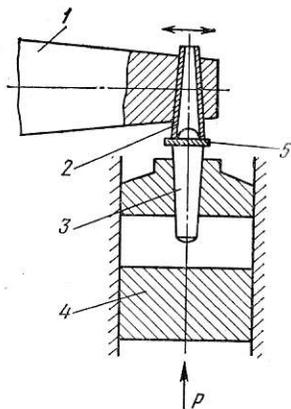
Ультразвуковая сварка по контуру:
